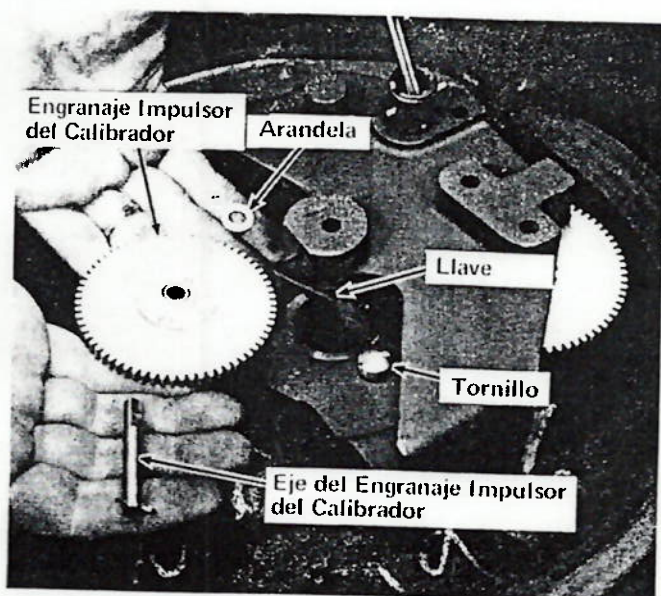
REMOCIÓN DEL EJE Y DEL ENGRANAJE IMPULSOR.
